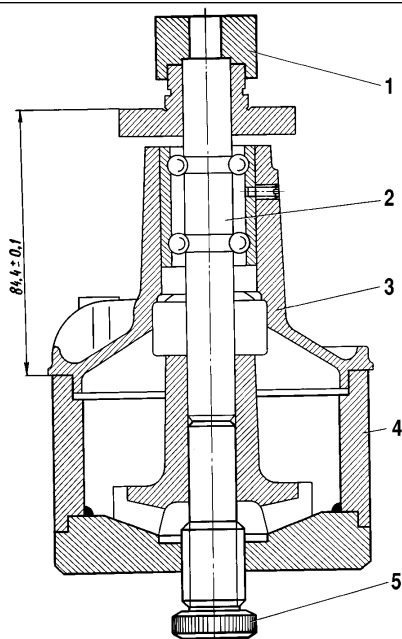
Aufpressen des Laufrades mit Vorrichtung A.60430 auf Pumpenwelle :
